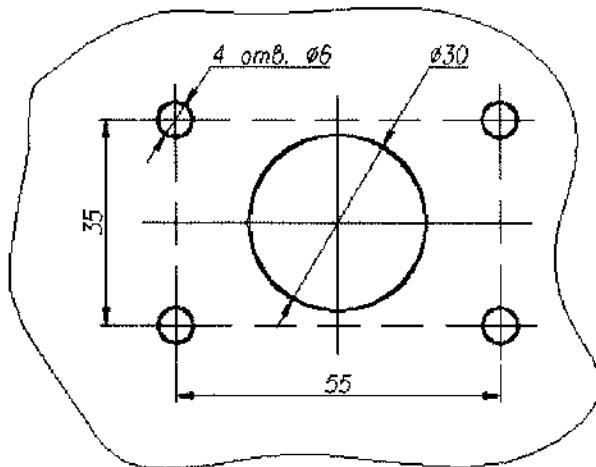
Размеры и взаимное расположение отверстий в установочной поверхности
